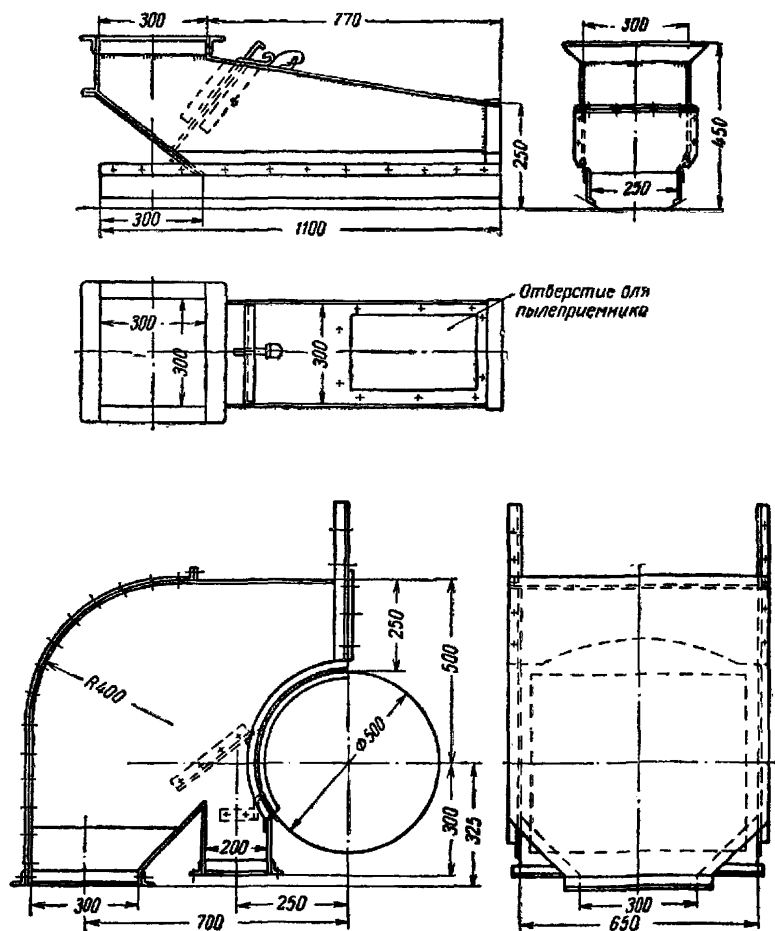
Насыпной лоток для ленты шириной 500—600 мм. Сбрасывающая коробка для ленты шириной 500—600 мм
